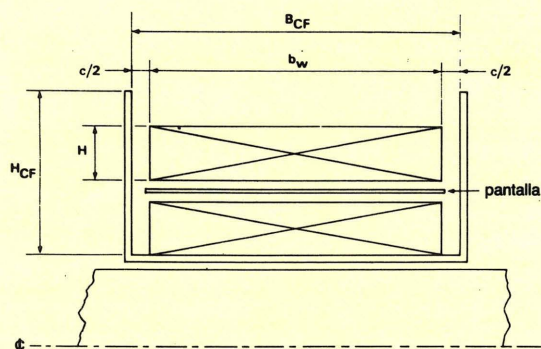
Definición de las dimensiones del carrete y el devanado.
